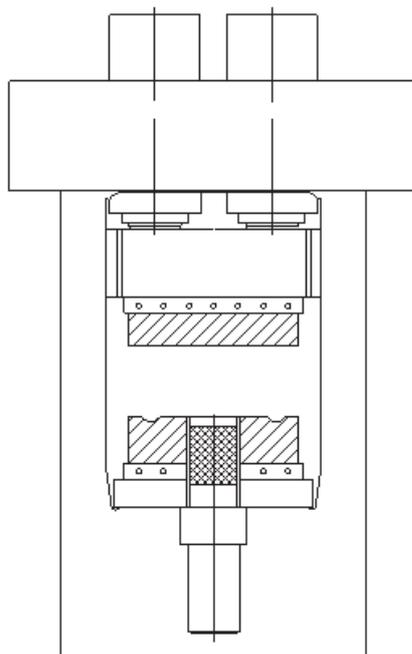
Presse zum Spritzpressen mit separatem Zylinder und mit Formmasse im separaten Hohlraum
